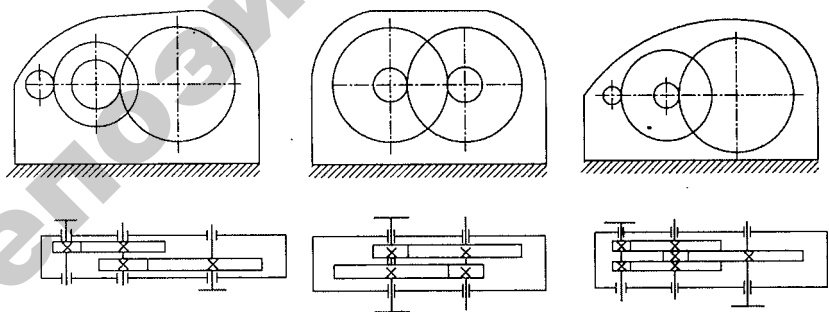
Цилиндрические двухступенчатые горизонтальные редукторы
